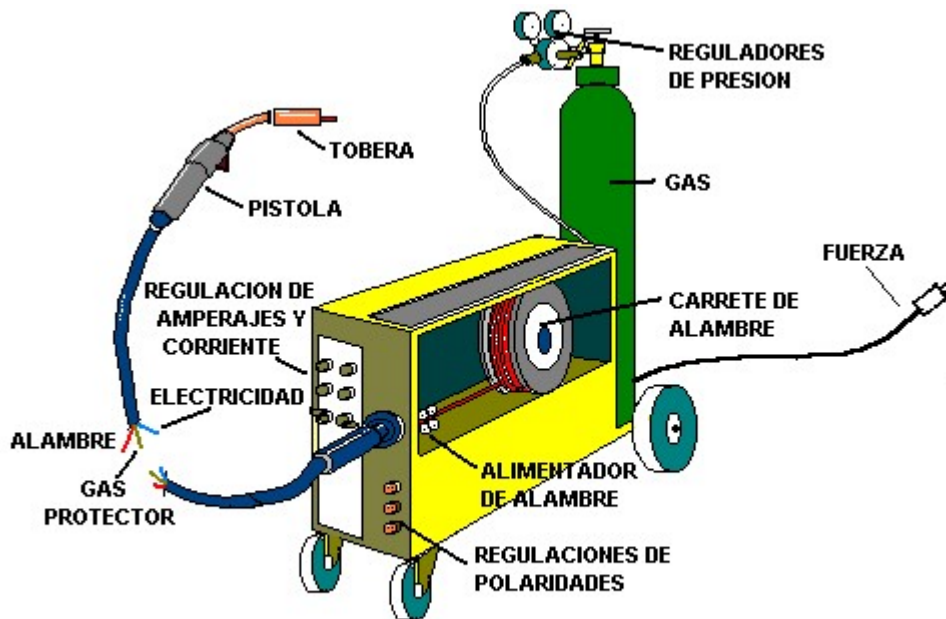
Esquema de los elementos que conforman un equipo de soldadura (GMAW). [19]
